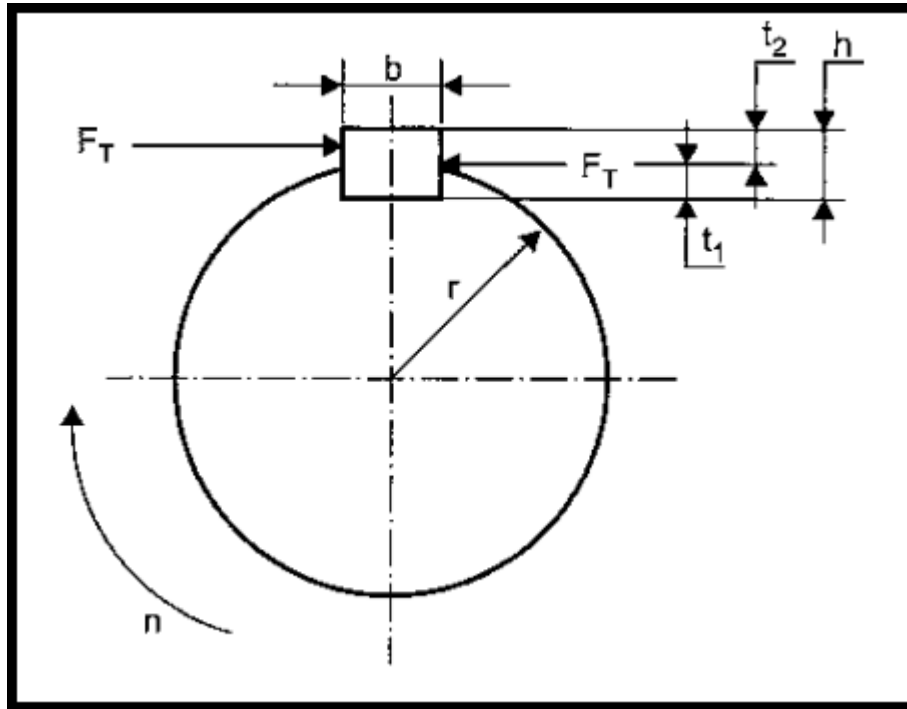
Dimensões da chaveta plana.(MELCONIAN, 2009).
